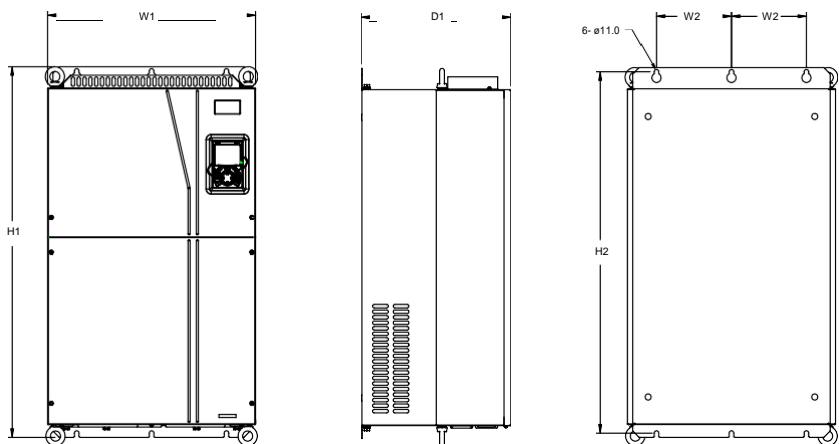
Схема настенного монтажа ПЧ 660 В, от 160 до 220 кВт
